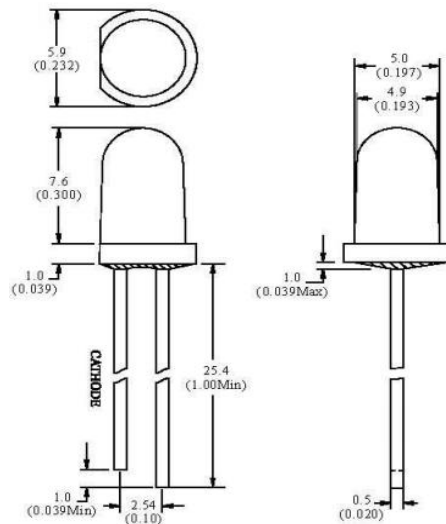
Зовнішній вигляд світлодіода типу L-1503GT "Kingbright"
